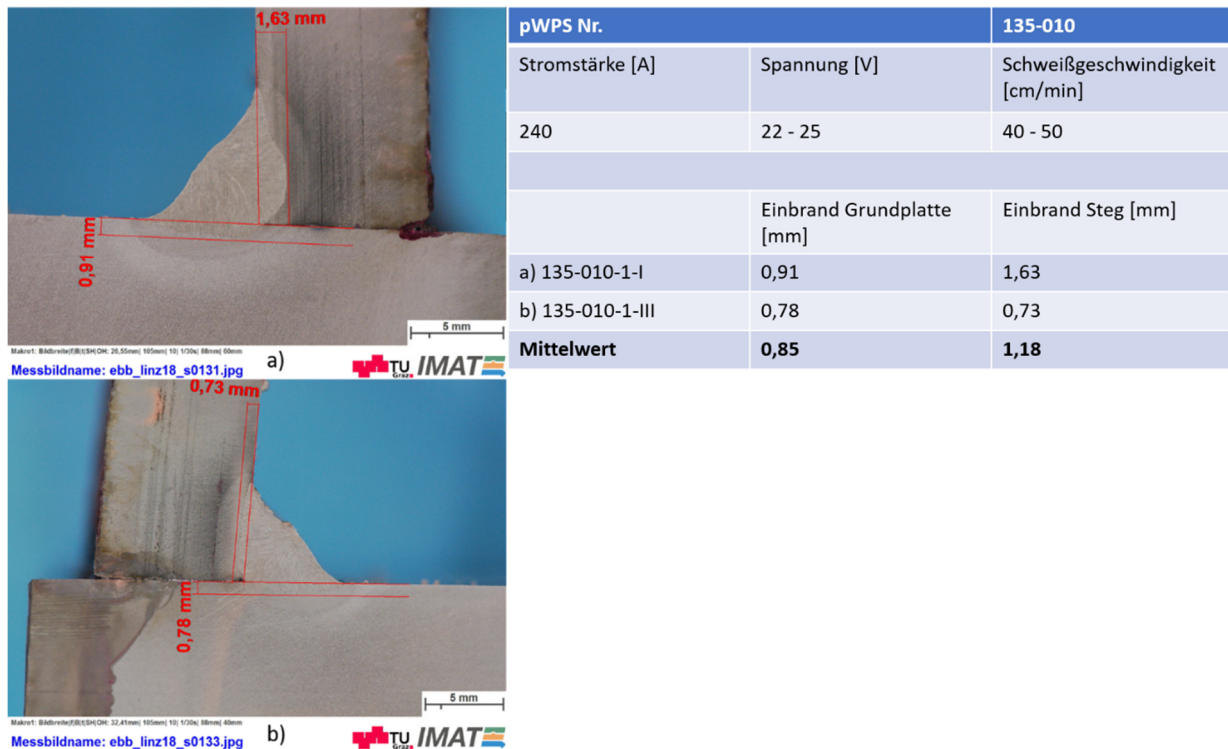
Kehlnahtschweißung – Grundplatte S235 JR / waagrecht – Altstahl / senkrecht; Auswertung der Schweißprobe 135-010-1; a) 135-010-1-I; b) 135-010-1-III
